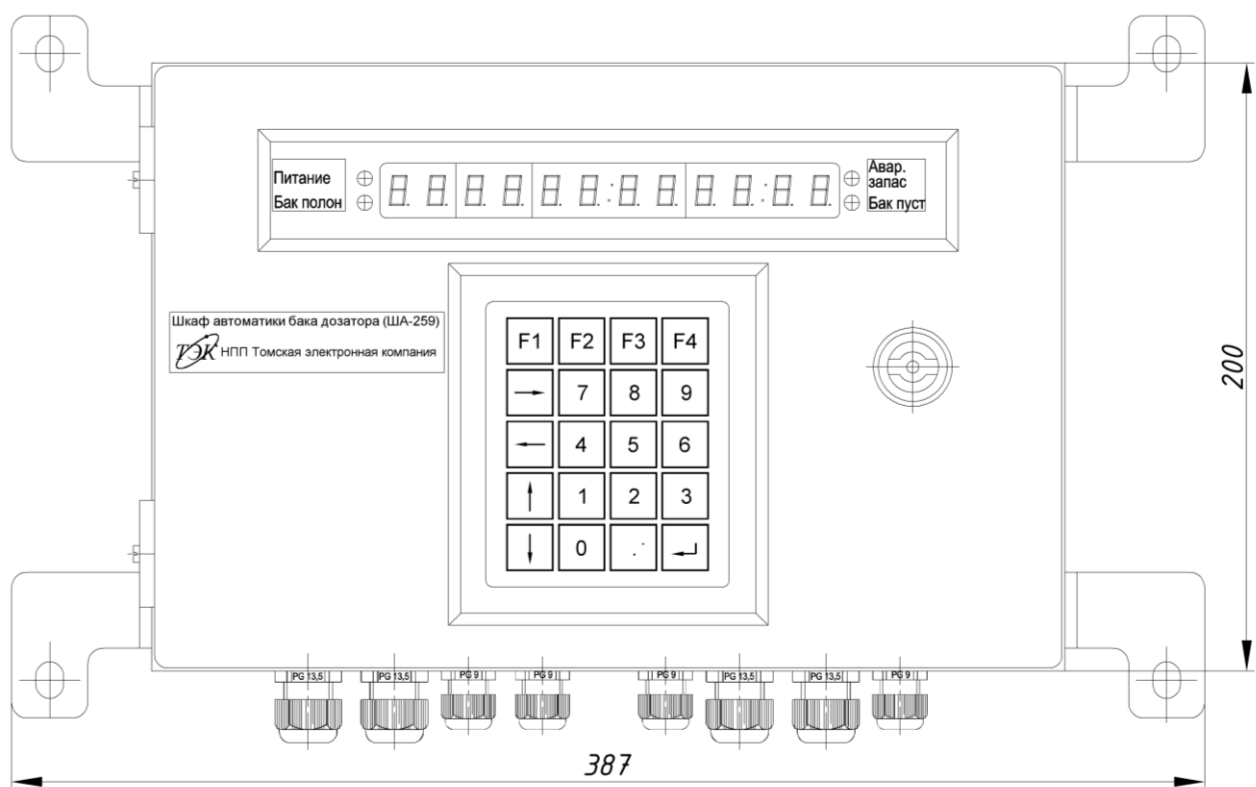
б - Внешний вид Шкафа автоматики бака-дозатора ША-259 исполнения
